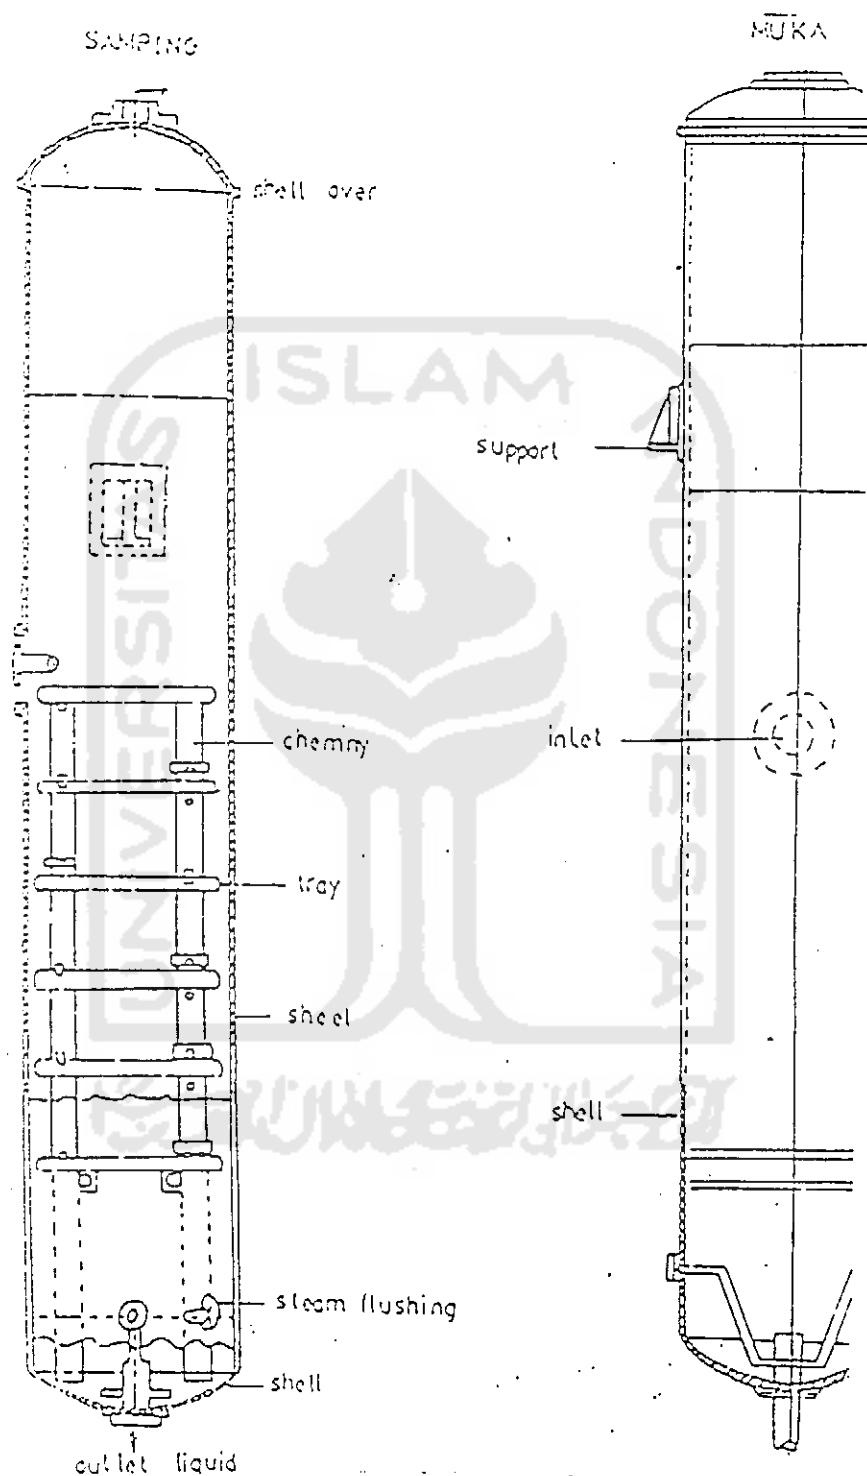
Penampang pada Menara Fraksinasi C-2.
